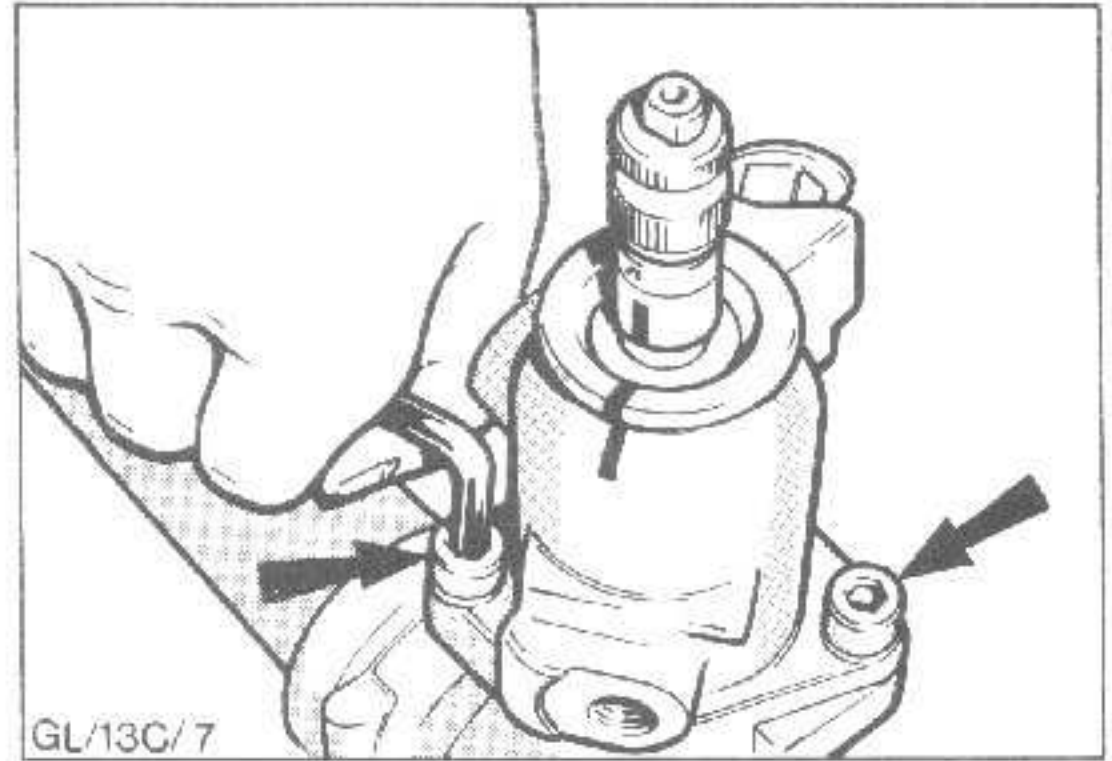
Ventilgehäuse abschrauben (Innensechskantschrauben)
